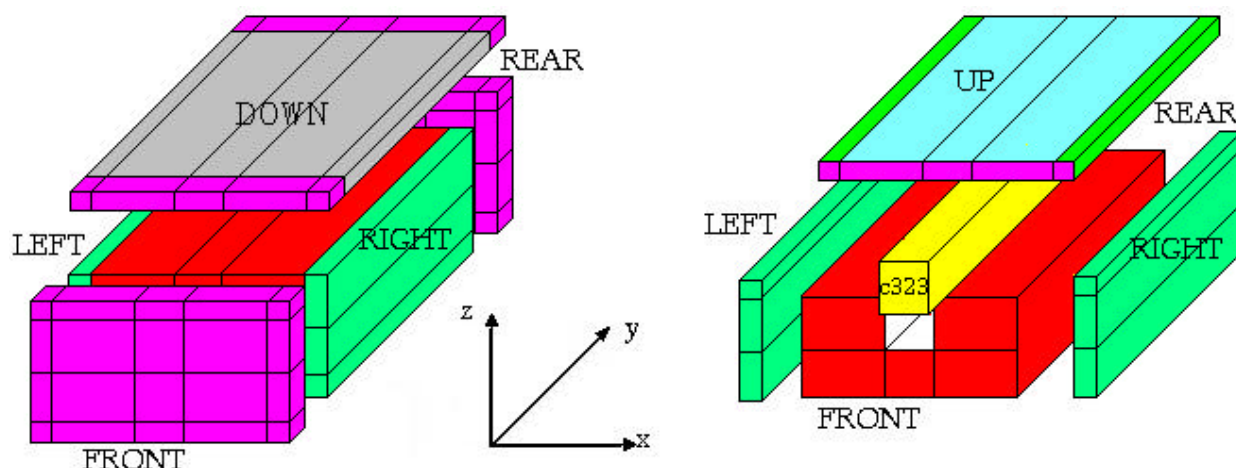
Usinagem de canal retangular com o primeiro e segundo “set-up”.
